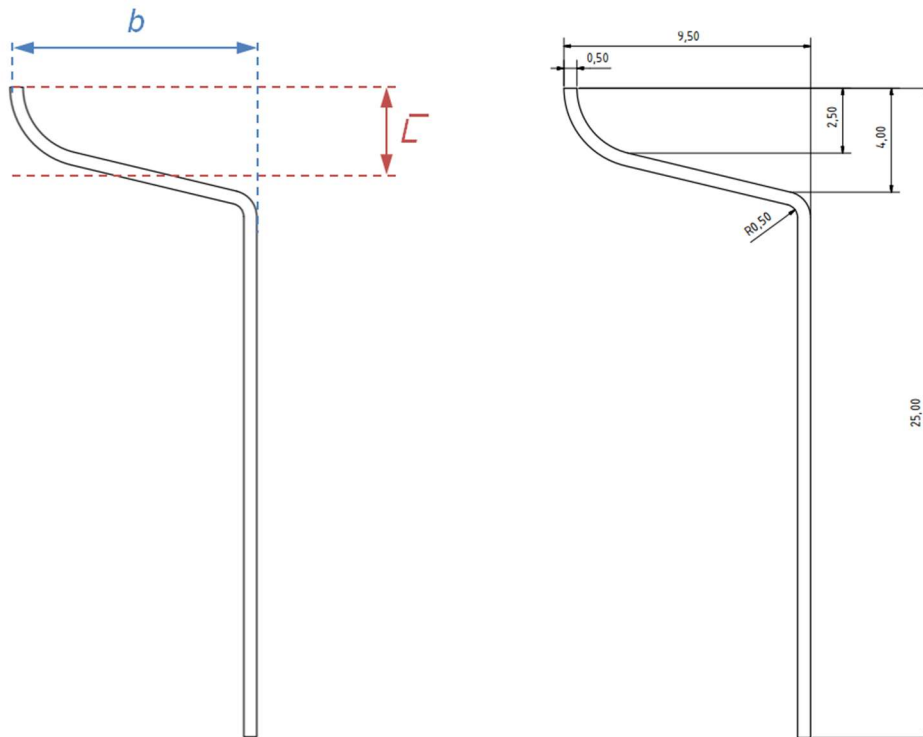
Zeichnungen der optimalen Geometrie des Ausgleichsblechs bemaßt
